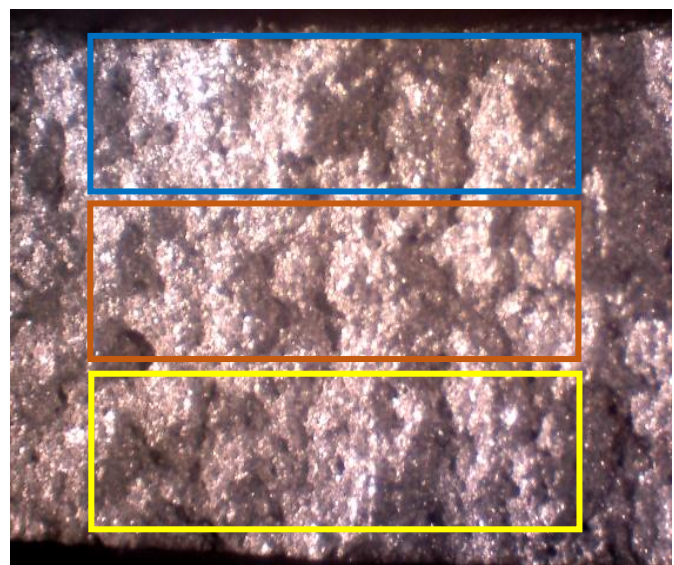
Fractura de la sección 2 de la probeta sin defecto utilizada en el ensayo de tracción.
